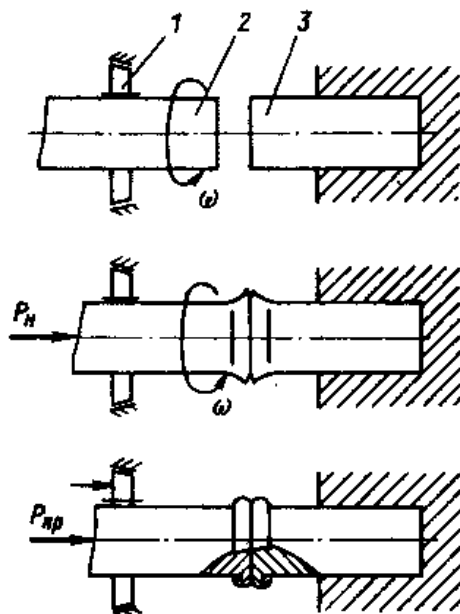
Схема сварки трением с непрерывным приводом:
